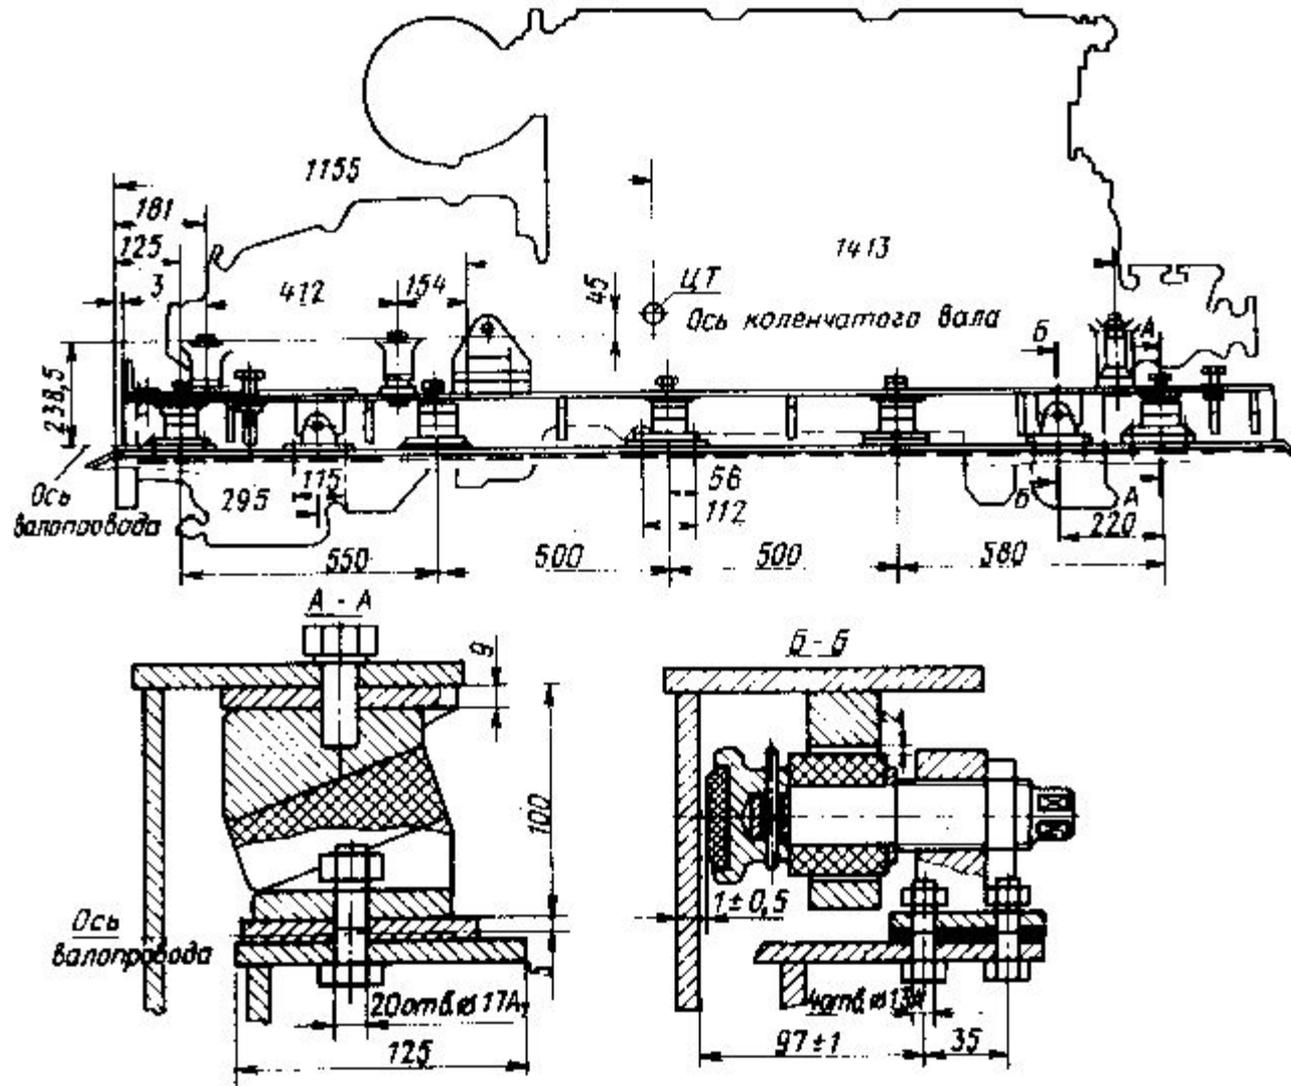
Типовая установка высокооборотного дизеля на виброизоляторах с узлами крепления виброизолятора и страховочного элемента.
